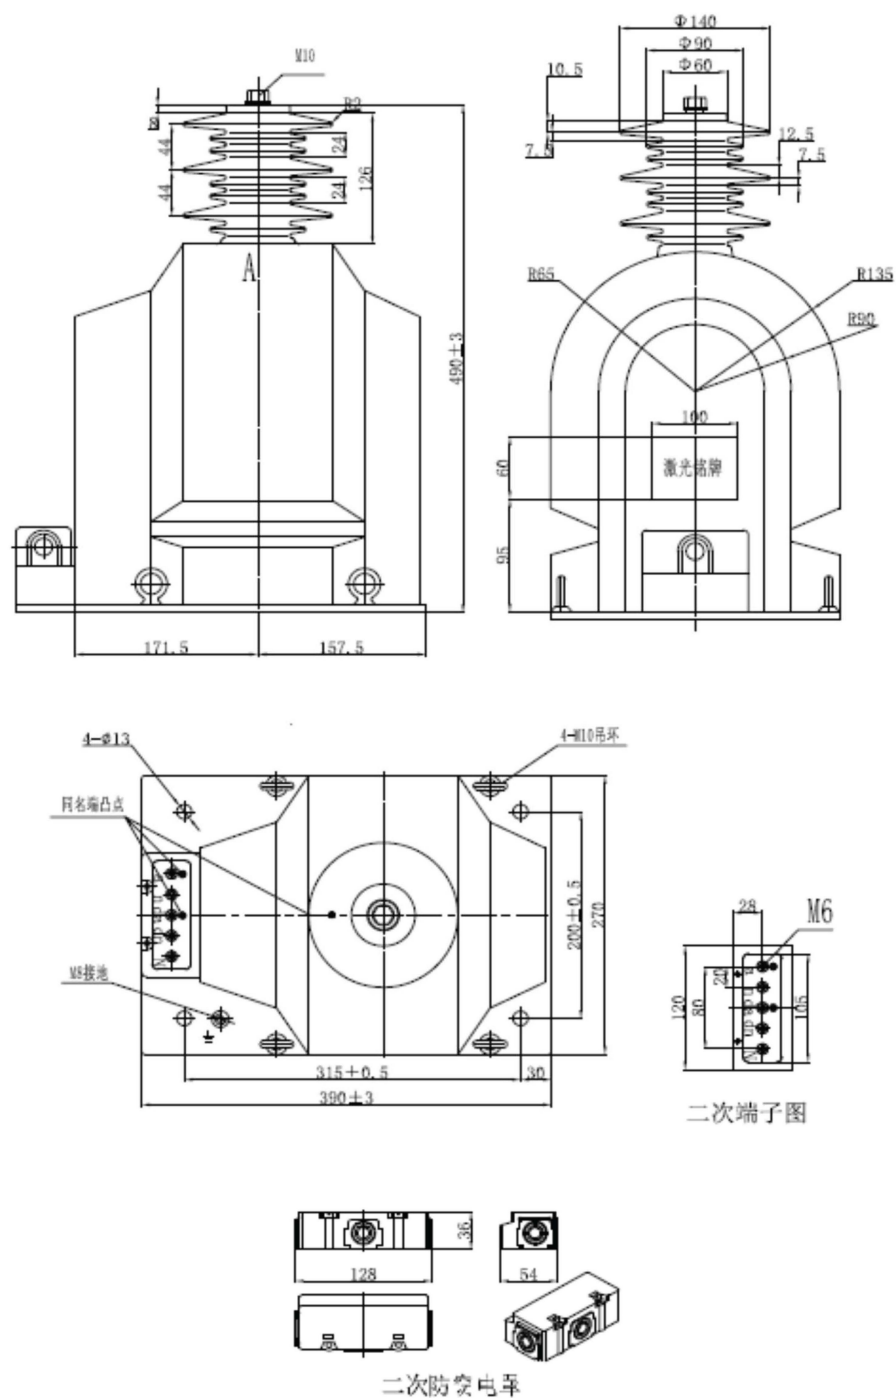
JDZYN-35型接地式电压互感器外形尺寸 (mm)
